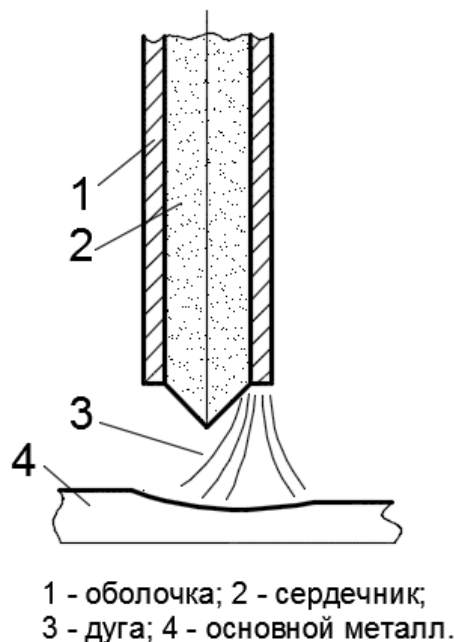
Схема горения дуги при сварке порошковой проволокой
